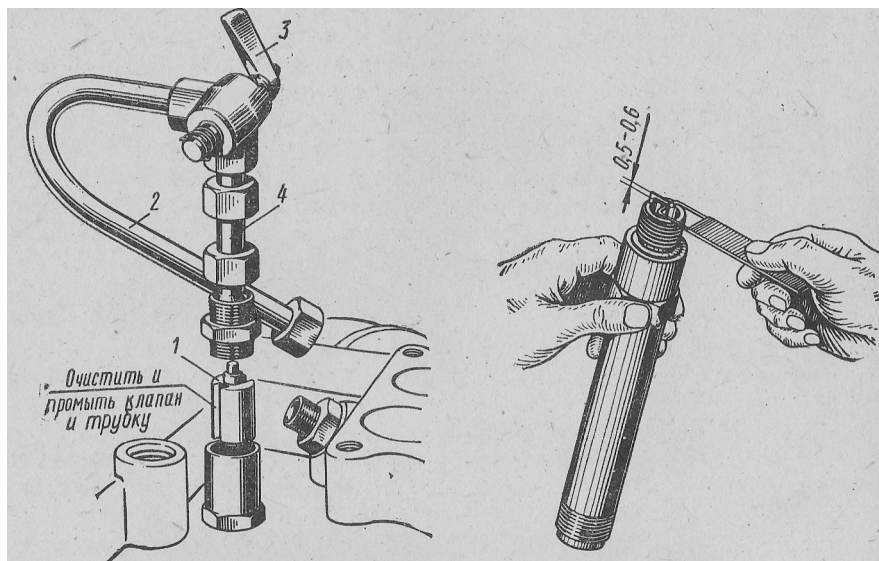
Очистка и промывка клапана вентиляции картера двигателя:
